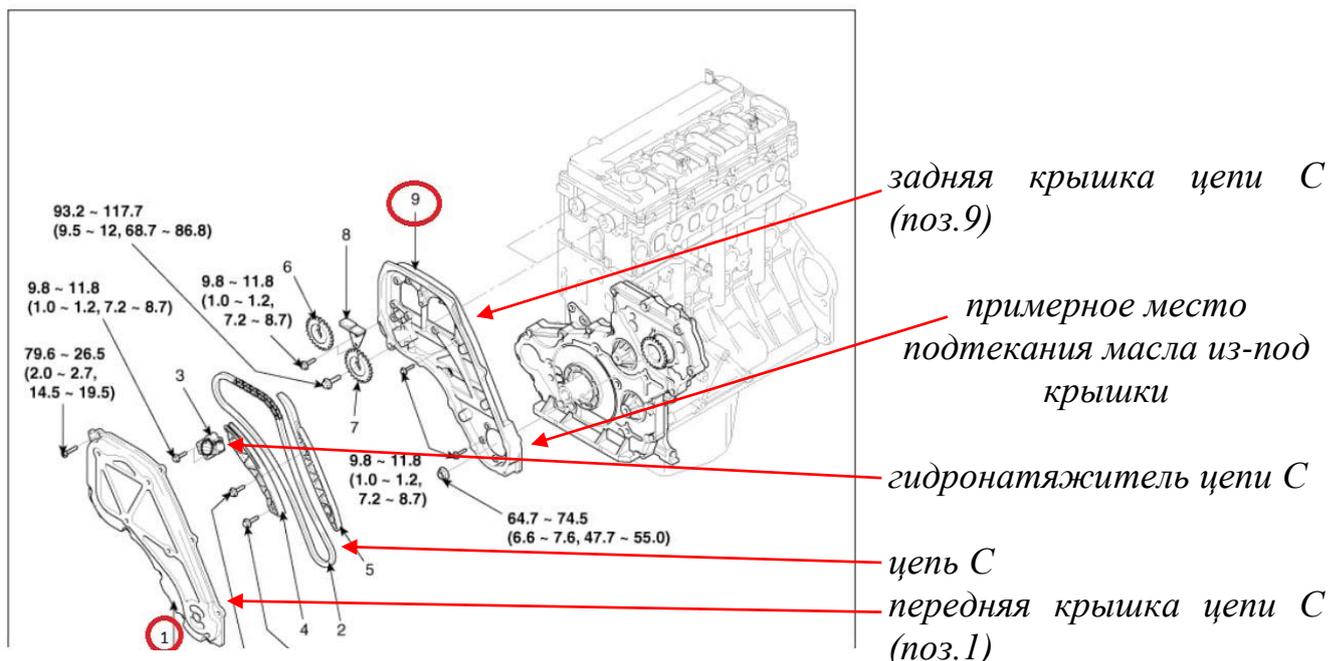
Цепи газораспределительного механизма двигателя, из ЕРС [3.6].
